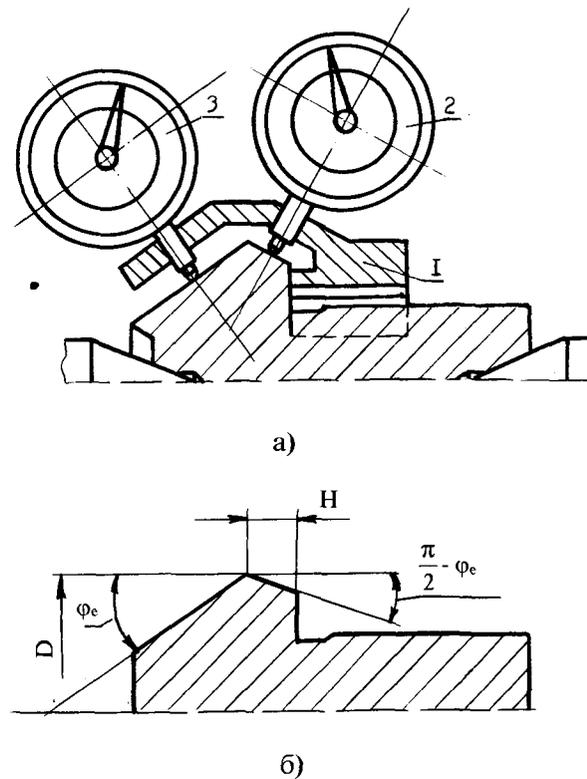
Приспособление для контроля наружного контура конических колес:
